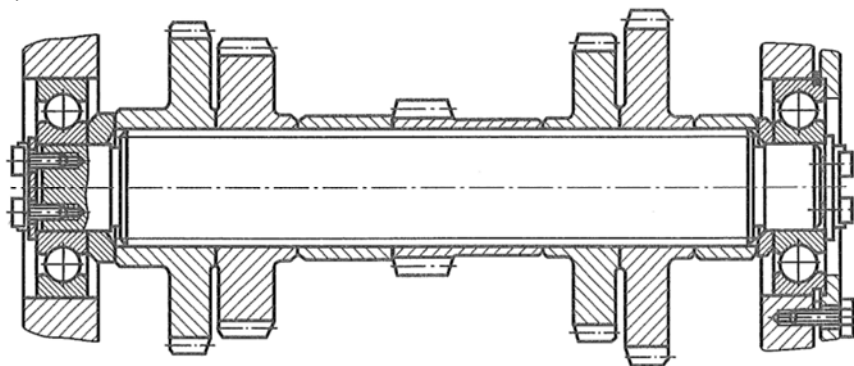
Пример установки вала на одной плавающей и одной фиксирующей опоре с одним подшипником в ней
